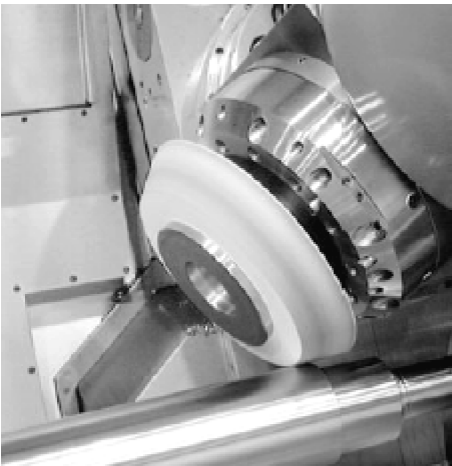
Шлифовальная головка к машинно-обрабатывающему центру MT2500SZ
